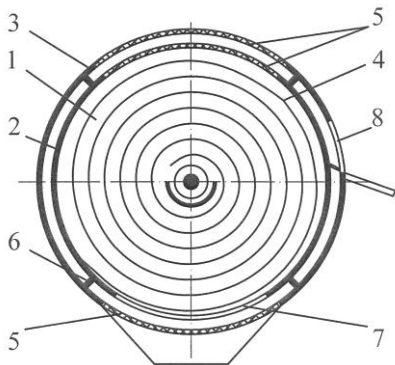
Сушарка з спіралеподібною поверхнею: 1 – сушильна камера; 2 – циліндрична обичайка; 3 – кожух; 4 – спіралеподібна поверхня; 5 – перфоровані вставки; 6 – полицка; 7 – вікно для вивантаження матеріалу; 8 – вивантажувальний отвір
